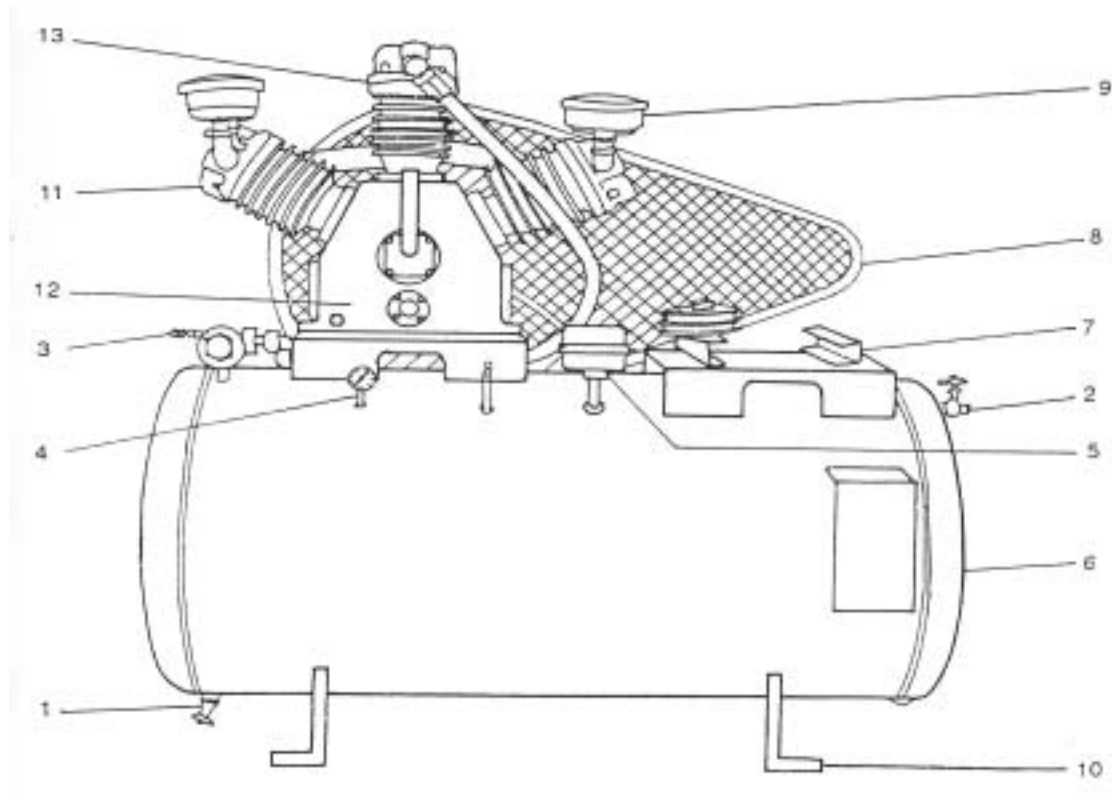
Partes exteriores de un compresor de émbolo oscilante
